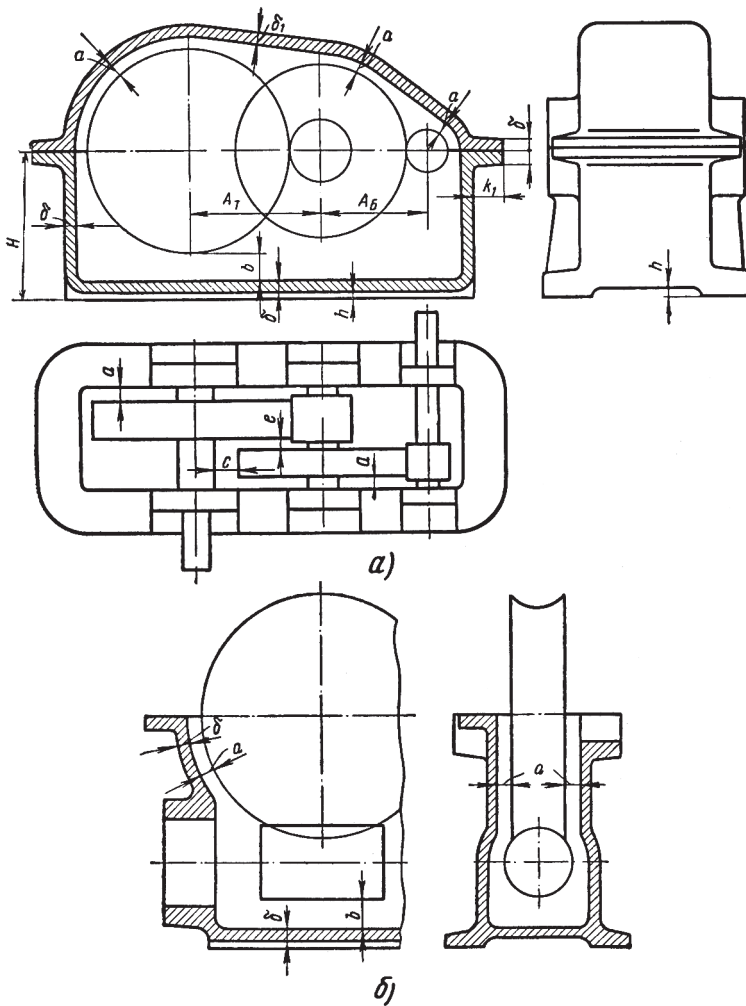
Определение конструктивных элементов: а – зубчатого редуктора; б – червячного редуктора
